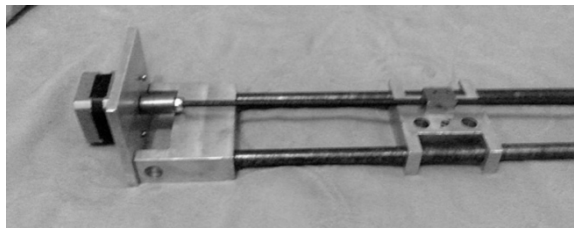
Montagem do eixo de transmissão para atuador linear do eixo Y.
